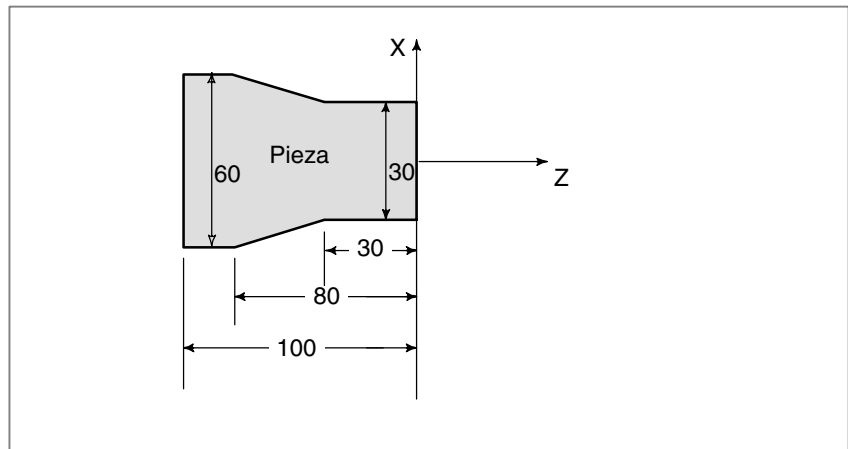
(e) Coordenadas y dimensiones en el plano de la pieza
